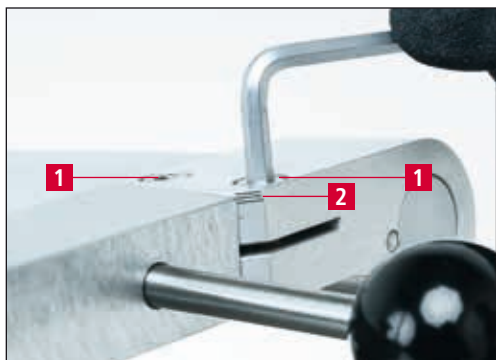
Поворот приспособления для заточки дисковых ножей
